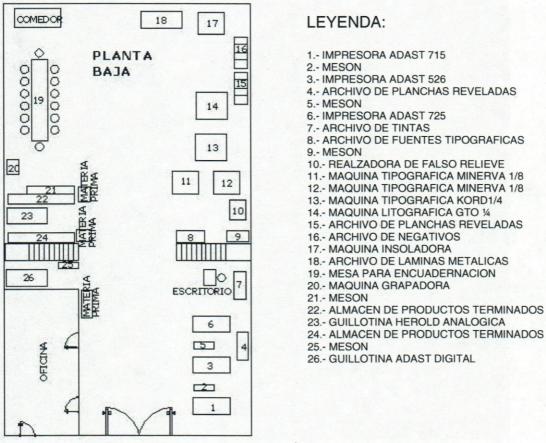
Croquis actual de ubicación de maquinaria en Planta Baja
